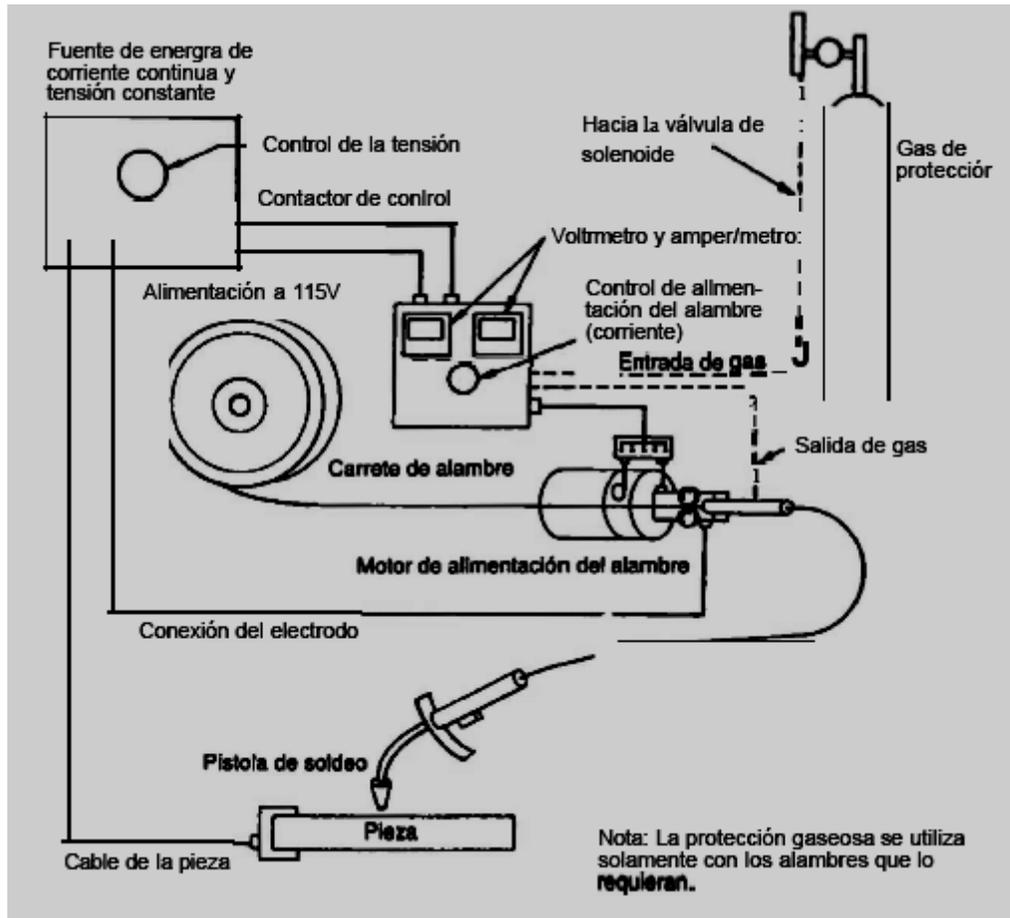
Equipo para soldadura por arco con alambre tubular.
